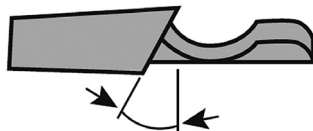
Определение угла заточки режущего зуба по горизонтали
